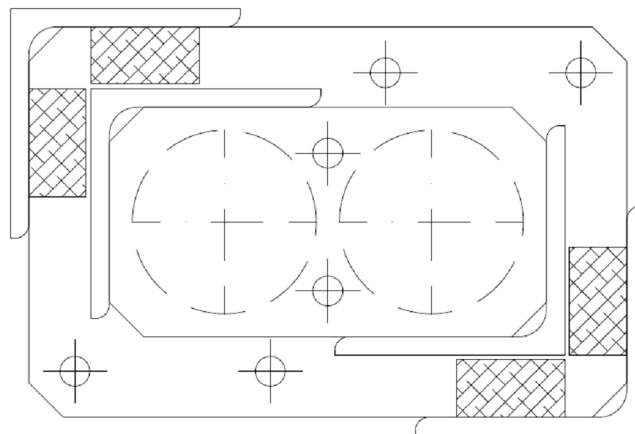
ó Plano amortiguador proyecto real 5. Vista en planta
